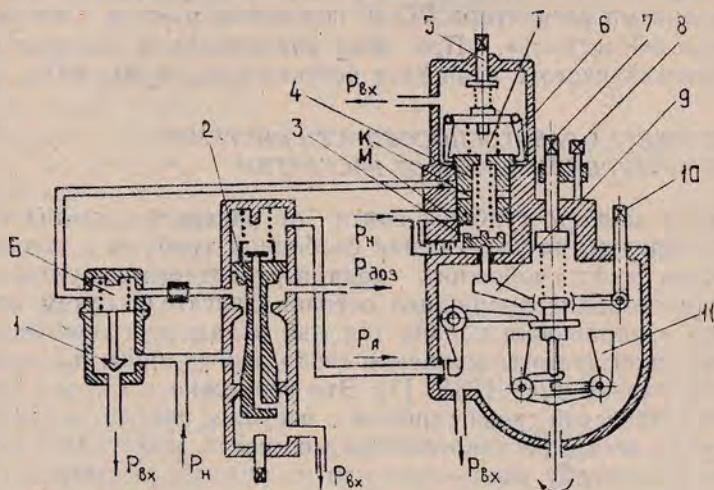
Схема работы системы защиты турбины винта от раскрутки: 1 — клапан постоянного перепада давления; 2 — дозирующая игла; 3 — клапан слива; 4 — золотник аварийного останова; 5, 7, 10 — регулировочный винт; 6 — захваты; 8 — винт фиксации режима; 9 — рычаг; 11 — грузики; М, К, Т — отверстия
